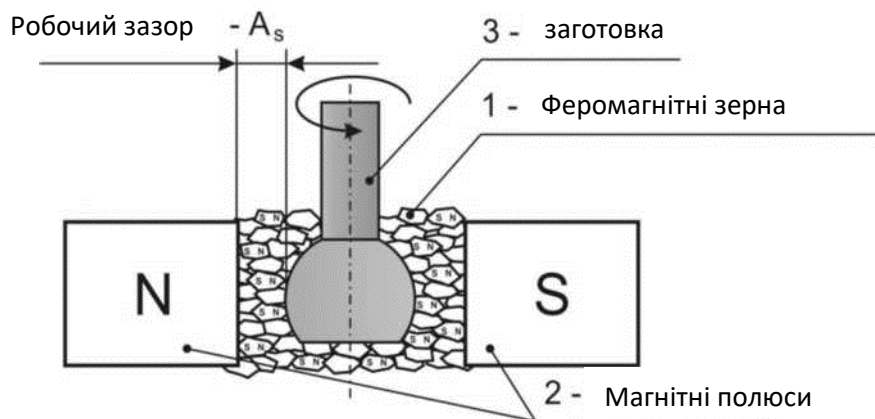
Схема МАО для обертально-симетричної заготовки
